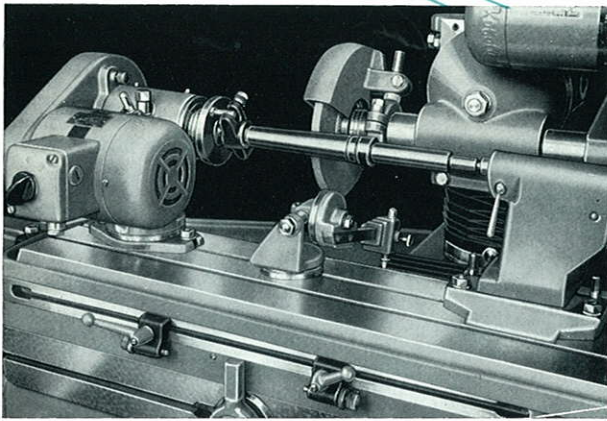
Außen-Rundschleifen zwischen Spitzen. Bild zeigt ferner die Schleifscheibenabziehvorrückung
